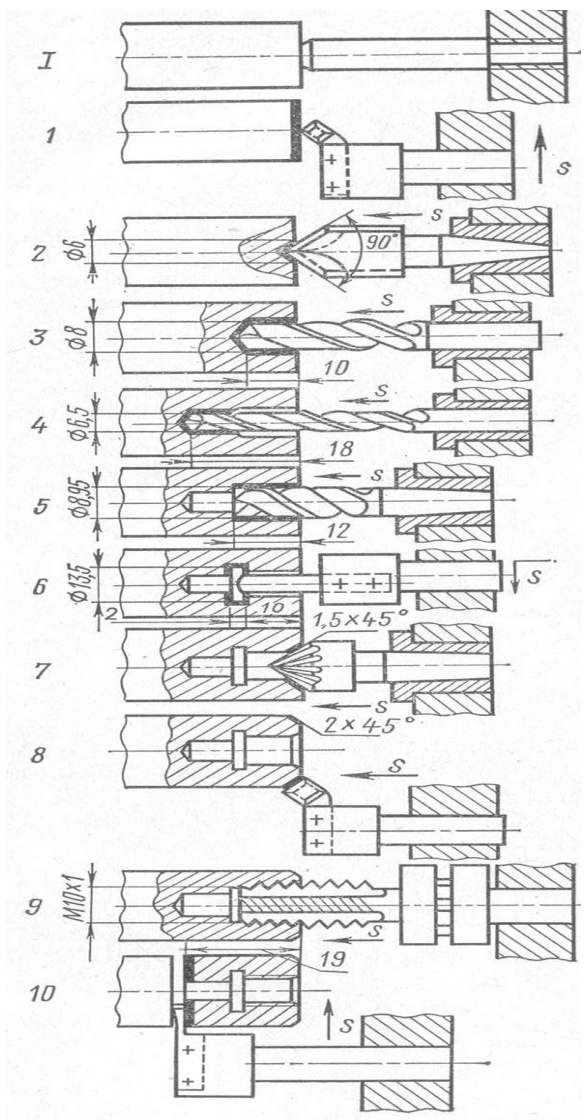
Схема налагодження верстата для виготовлення втулки
